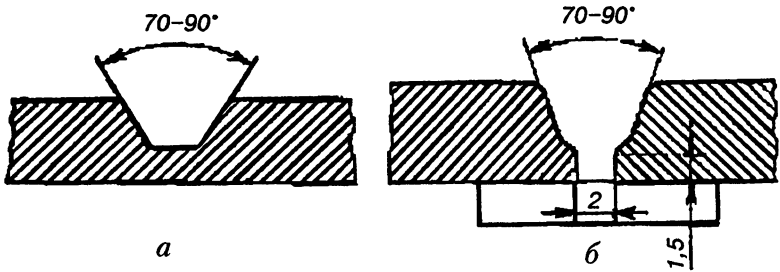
Профілі розчищених дефектів для паяння-зварювання чавунними прутками:
